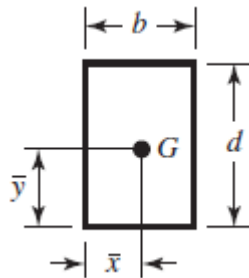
Patrón de soldadura para la estructura móvil
